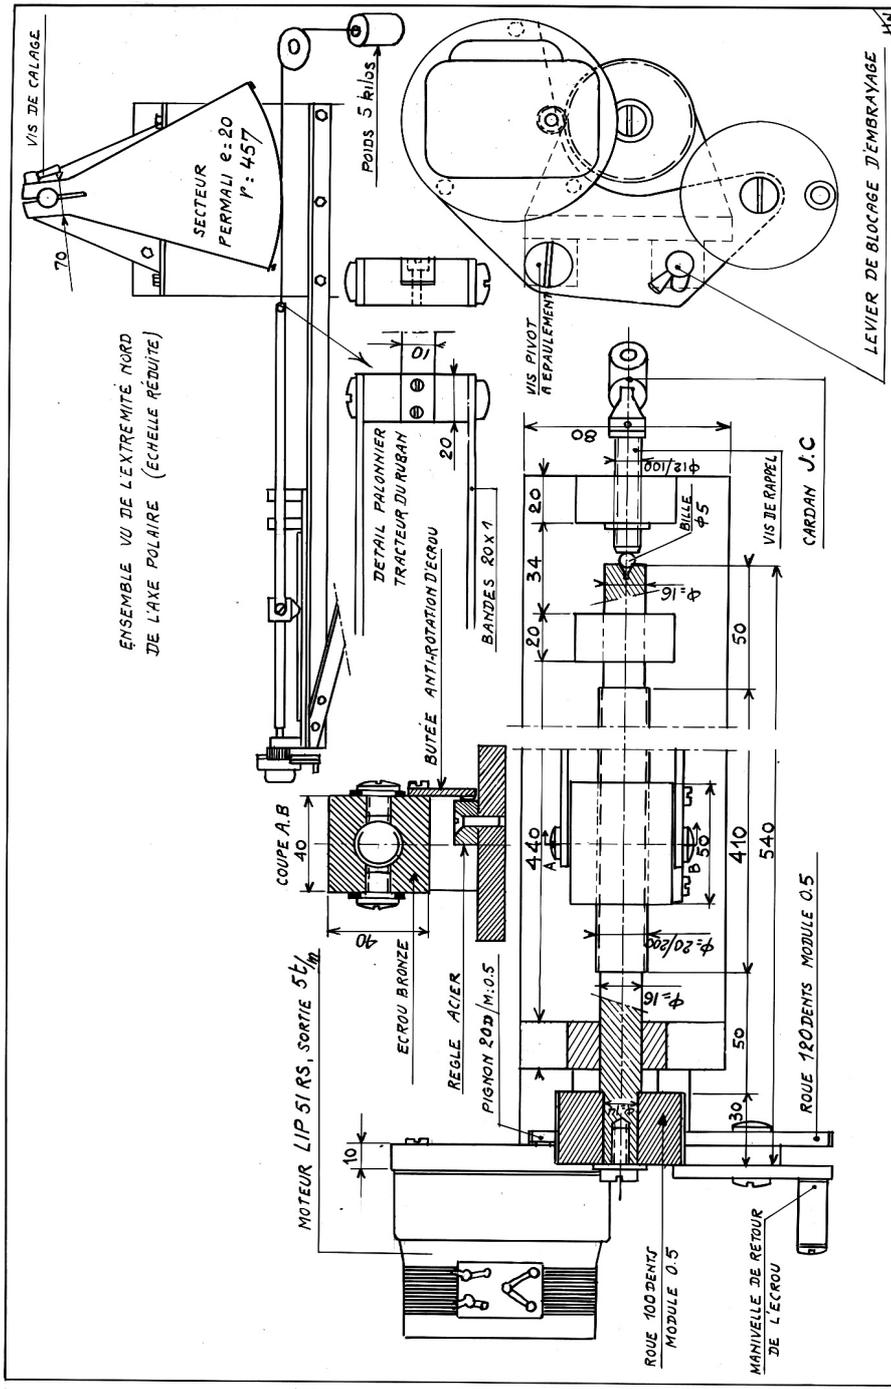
Disposition générale d'un entraînement par vis et secteur.
